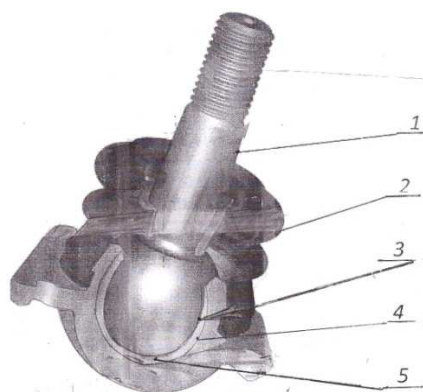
Вид шаровой опоры механизма подвески: 1 – стержень; 2 - уплотнительная манжета; 3 – охватываемая шаровая поверхность; 4 - зазор; 5 - охватываемая поверхность
